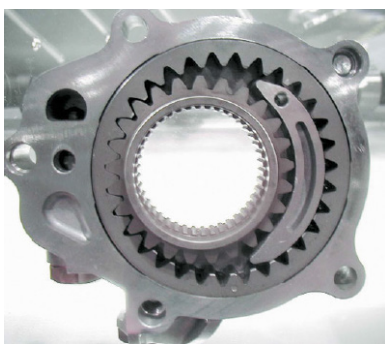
Типовой масляный насос с внутренним зубчатым зацеплением, установлен в передней крышке двигателя, и приводится в действие от коленчатого вала двигателя; источник: *Pearson Education, Inc.
